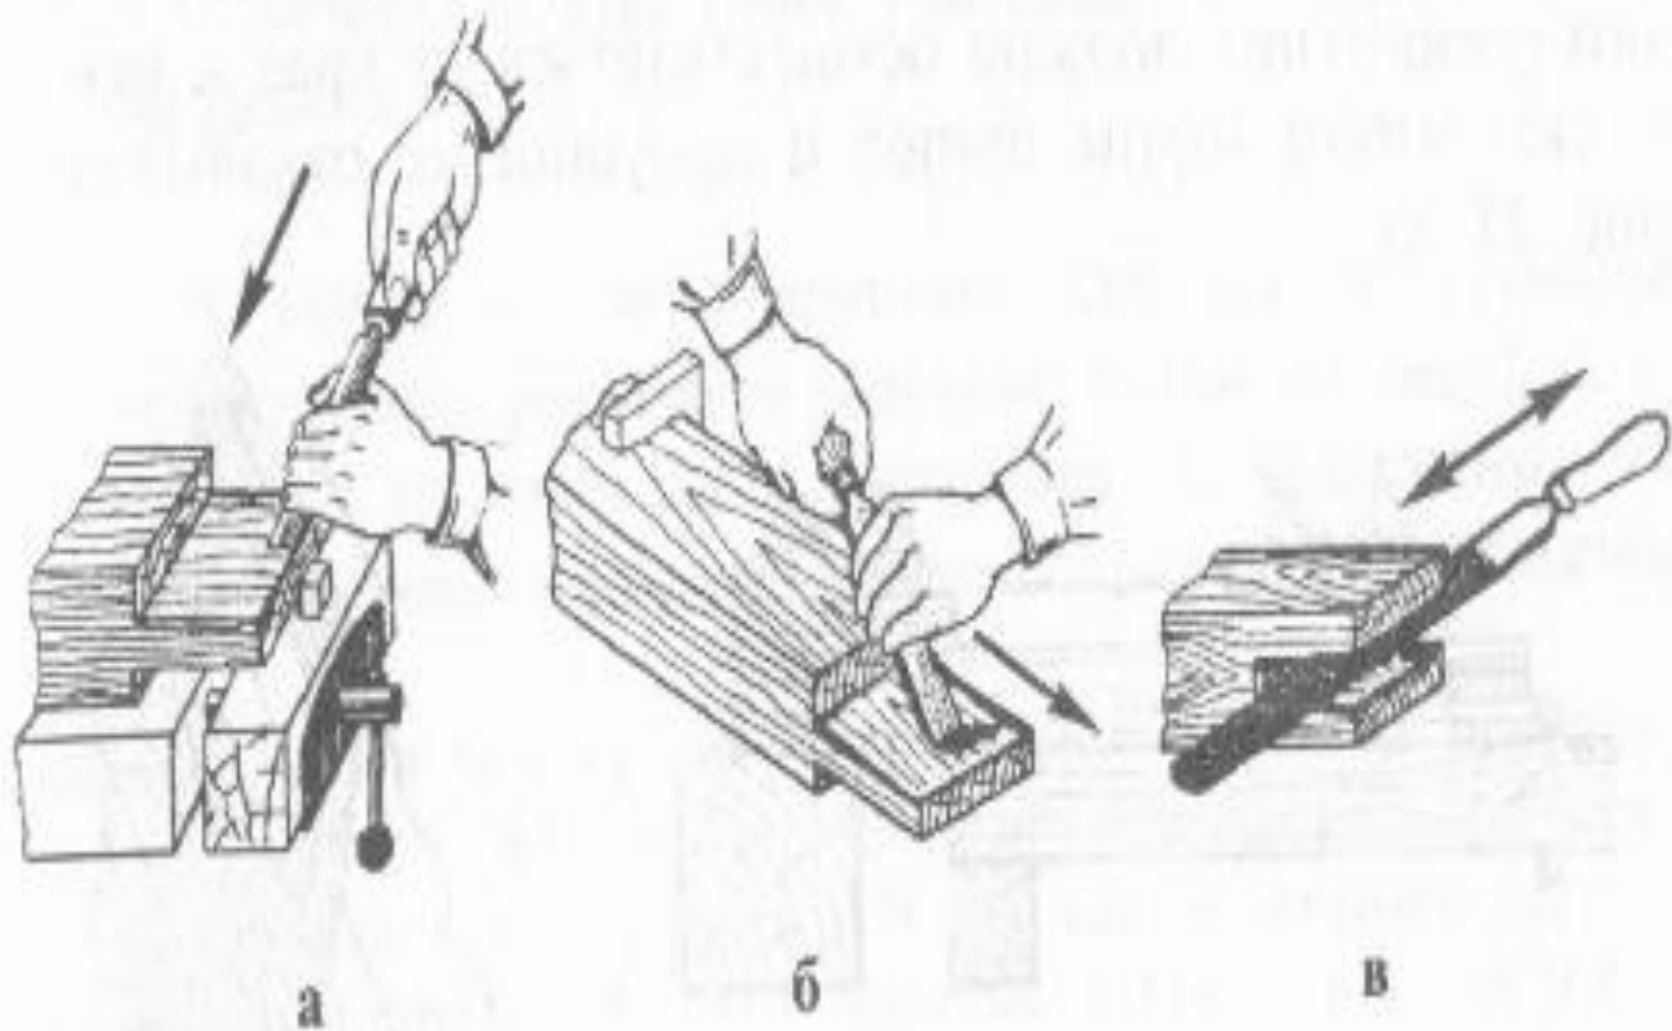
Обработка шипов и проушин в размер: а, б — стамеской;
